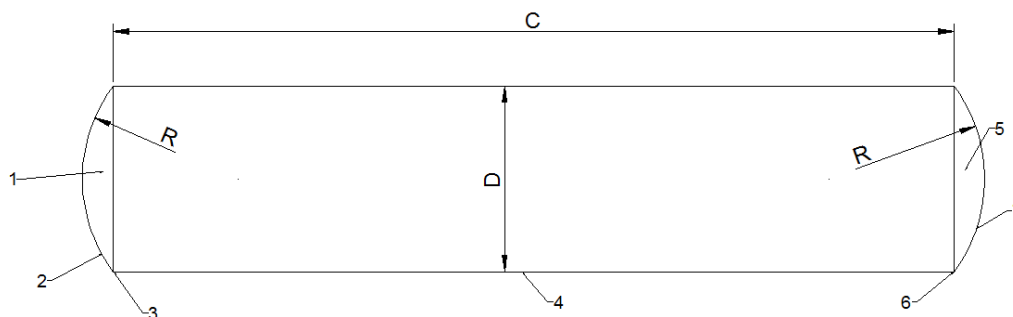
Конструктивно-силовая схема несущей топливной ёмкости первой ступени
